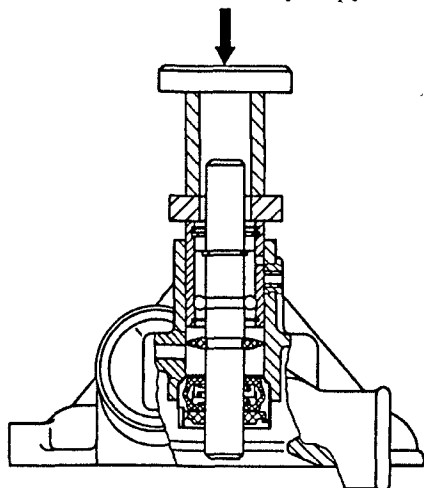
Запрессовка подшипника с валиком водяного насоса
